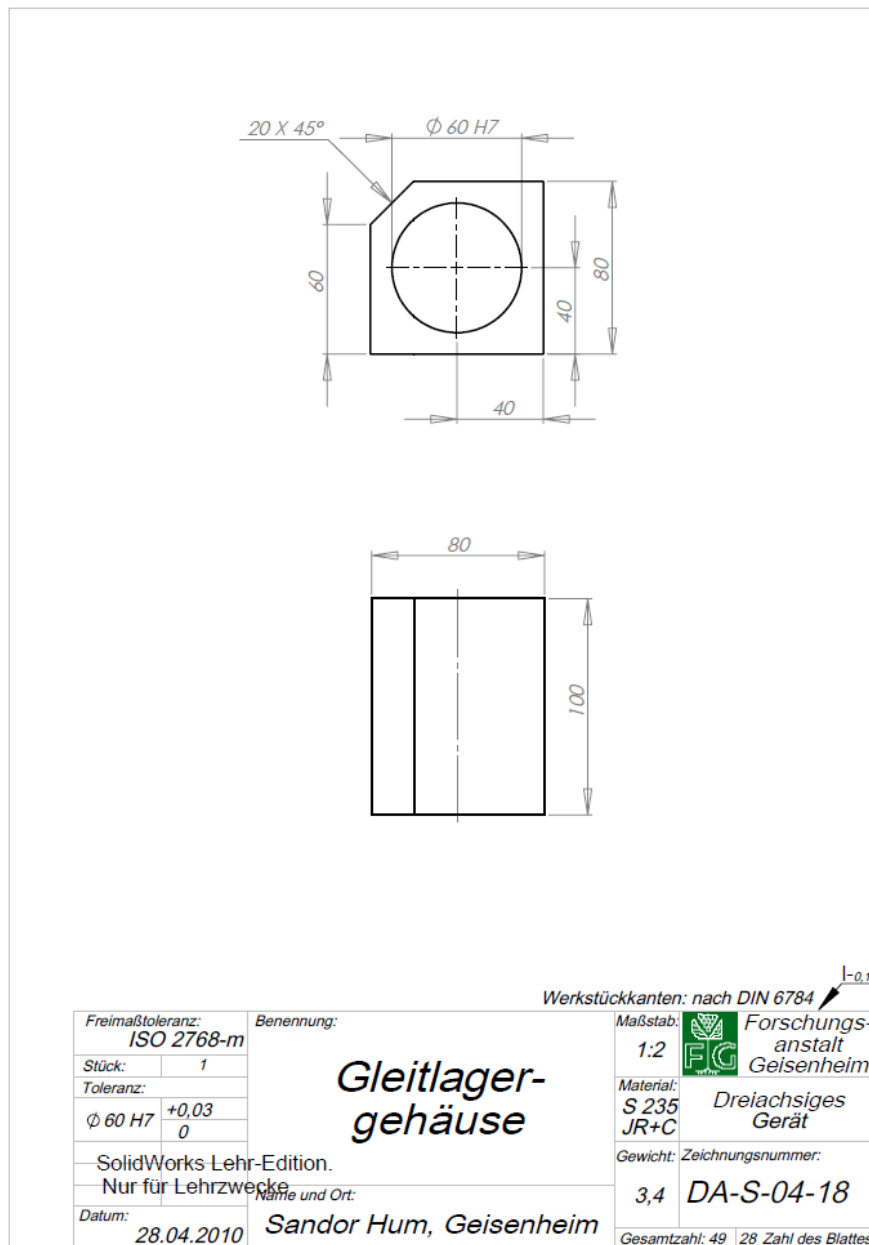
Bauteilzeichnung des Gleitlagergehäuses
